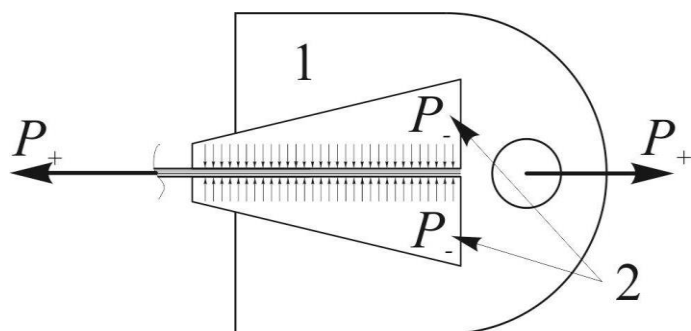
Самозатягивающийся захват. 1 – корпус захвата, 2 – губки, между которыми зажимается образец
